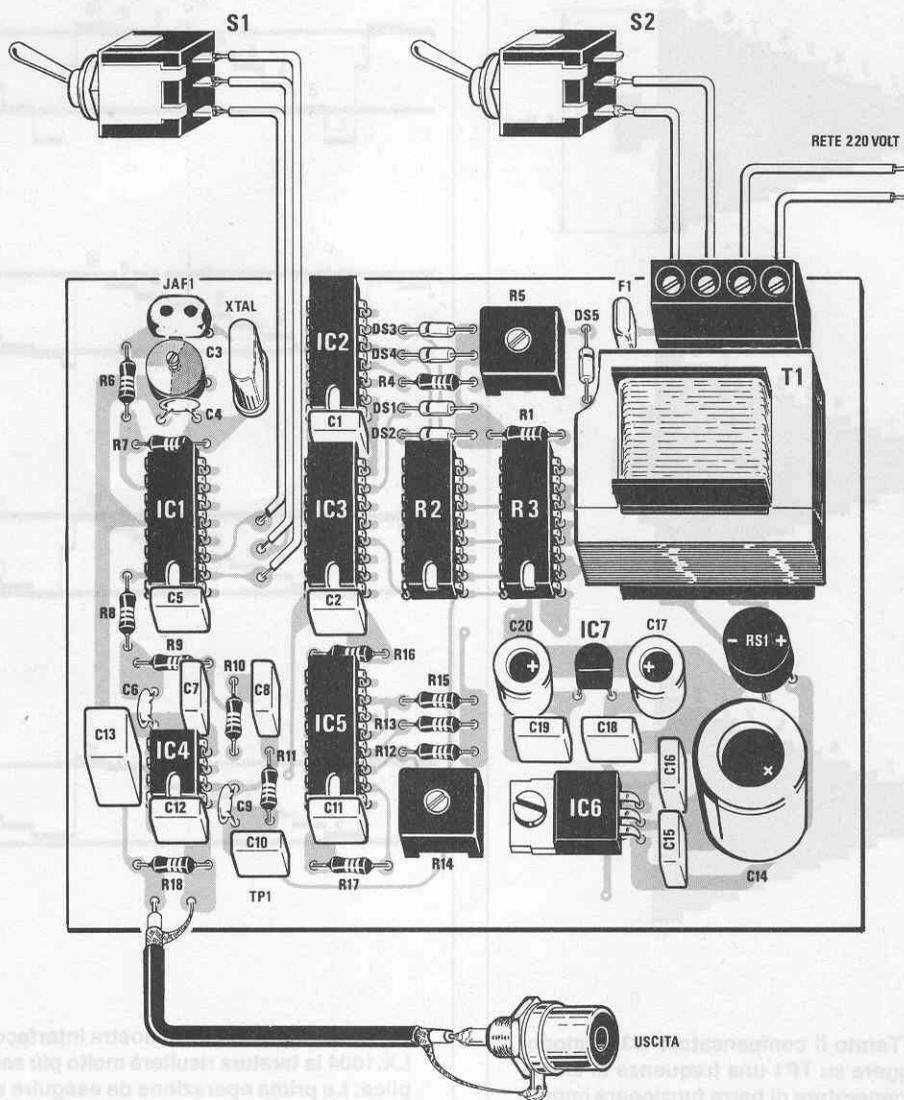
Schema pratico di montaggio del Generatore della scala dei Grigi. Come potete notare, il trasformatore risulta direttamente fissato sullo stampato e per collegare i due fili della tensione di rete ed il relativo interruttore di accensione viene utilizzata una morsettiere a 4 poli. Sul lato sinistro di tale morsettiere è presente il fusibile autoripristinante F1. In basso, vicino al condensatore C10, è presente un terminale test-point (vedi TP1) che vi sarà utile per controllare tramite un frequenzimetro la frequenza generata dal quarzo.
